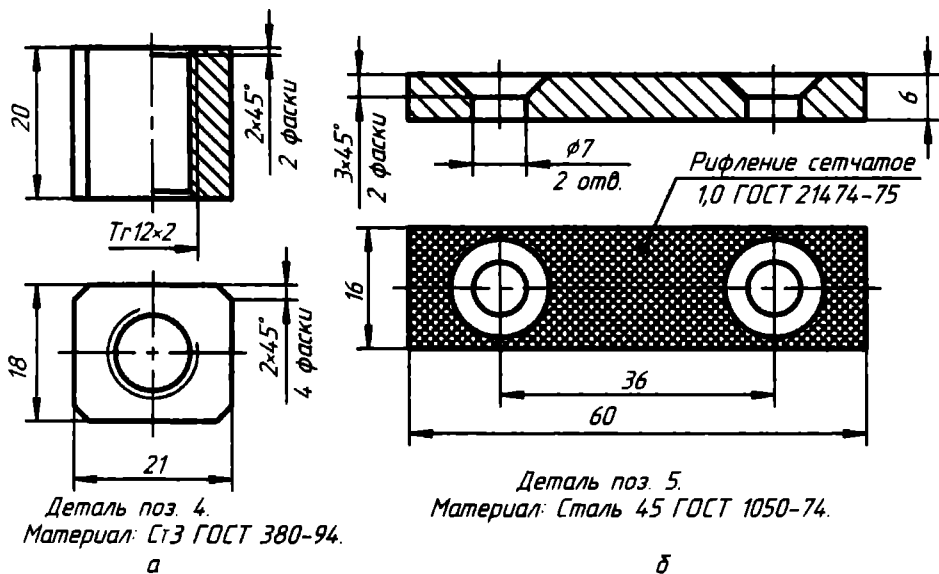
Чертежи: а — ходовой гайки; б — нагубника
